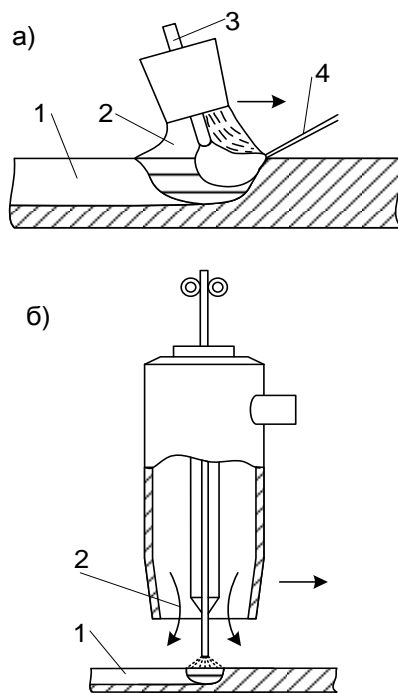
Схема дуговой сварки в защитном газе:
